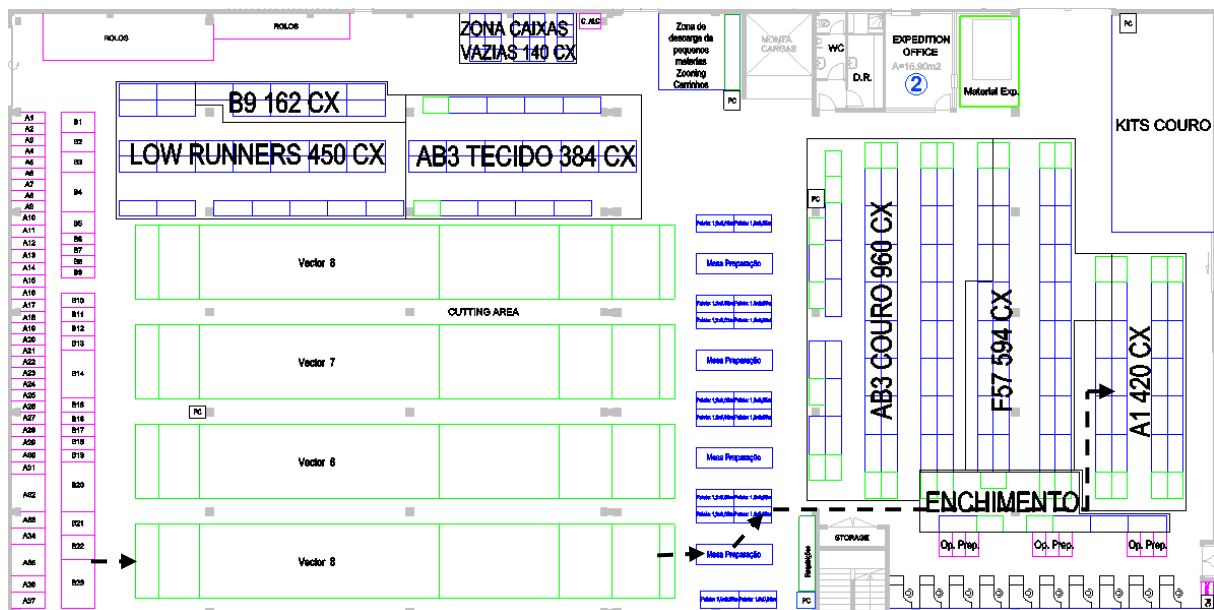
Segunda proposta layout - fluxo projeto A1 s/enchimento
